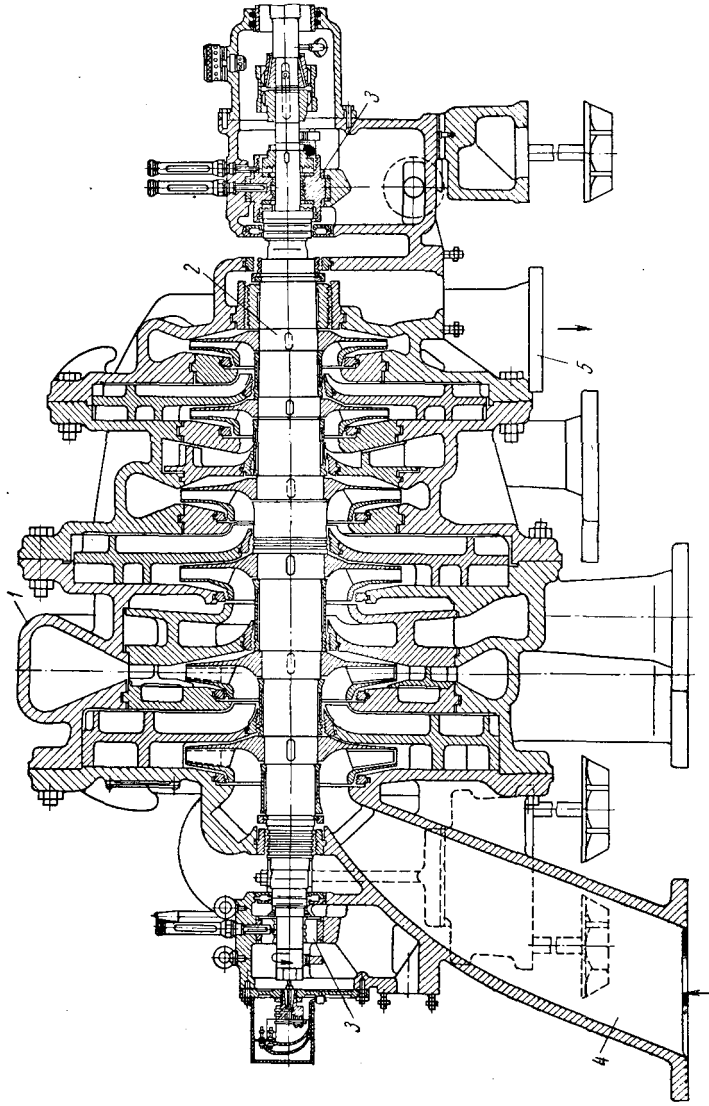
Продольный разрез турбокомпрессора К 250-61-2:
